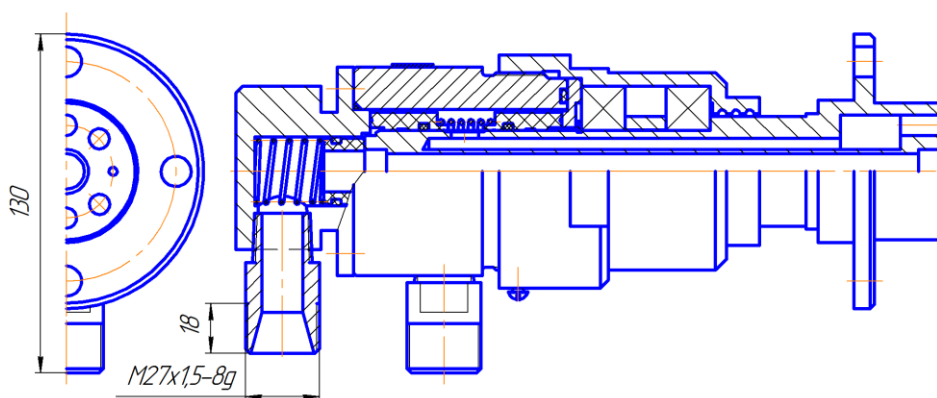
Вертлюжок сдвоенный БНГ.102.00.00-01
